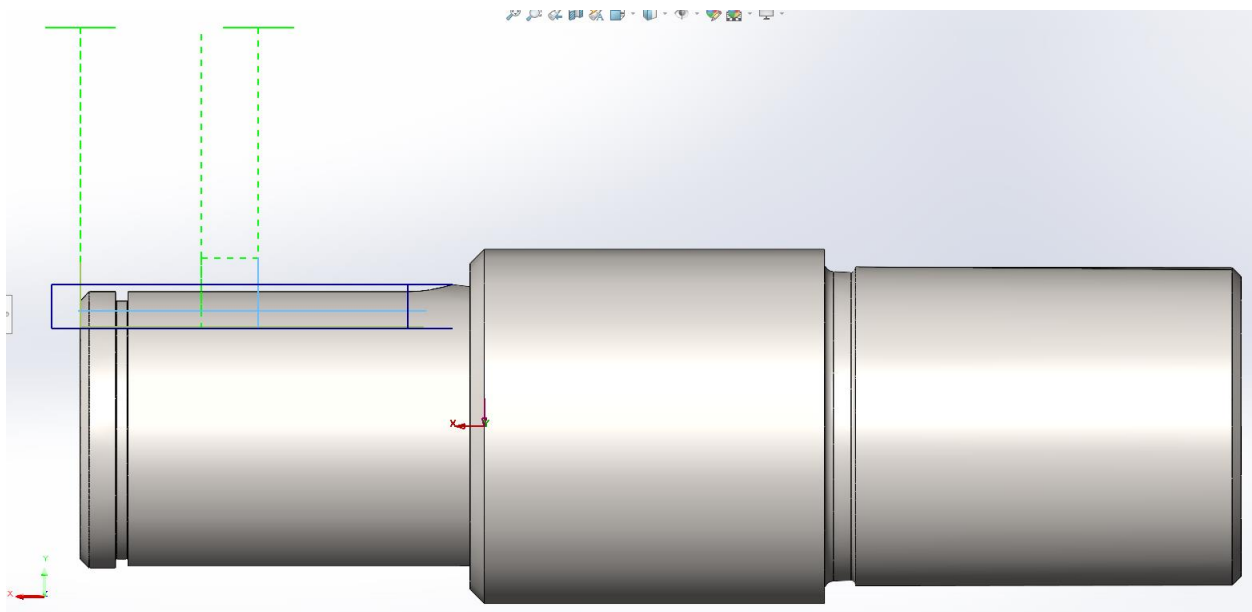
Траекторія руху фрези при чорновому та контурному фрезеруванні шпоночного пазу.
